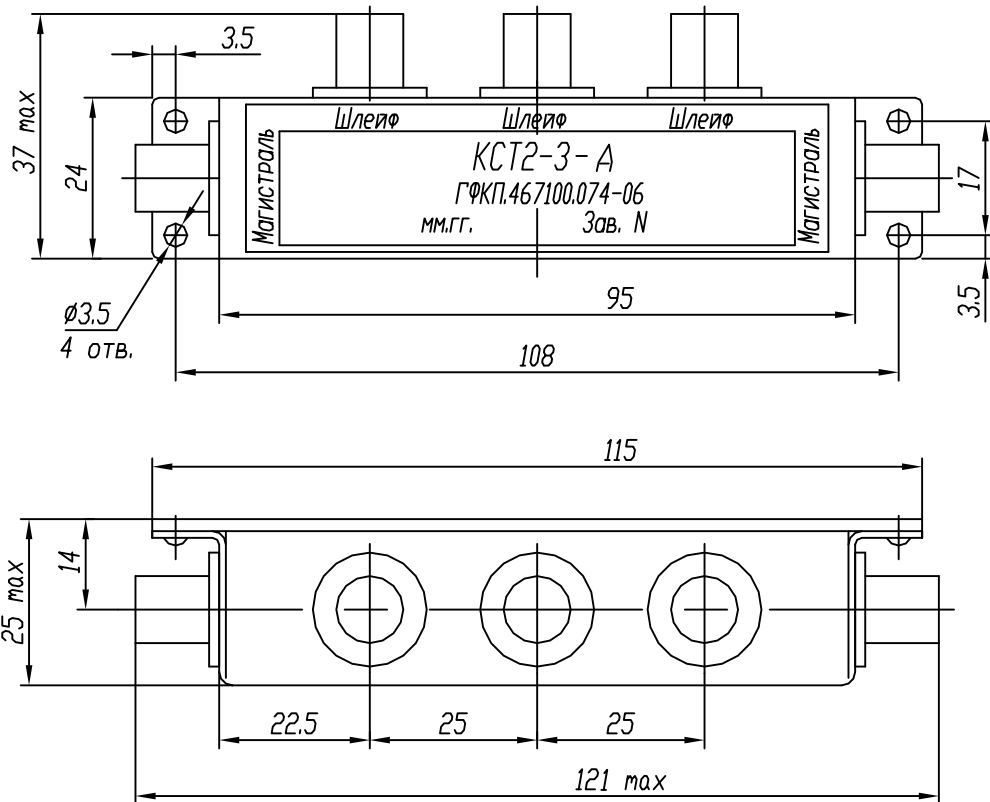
Габаритный чертеж коробки соединительной КСТ2-3
